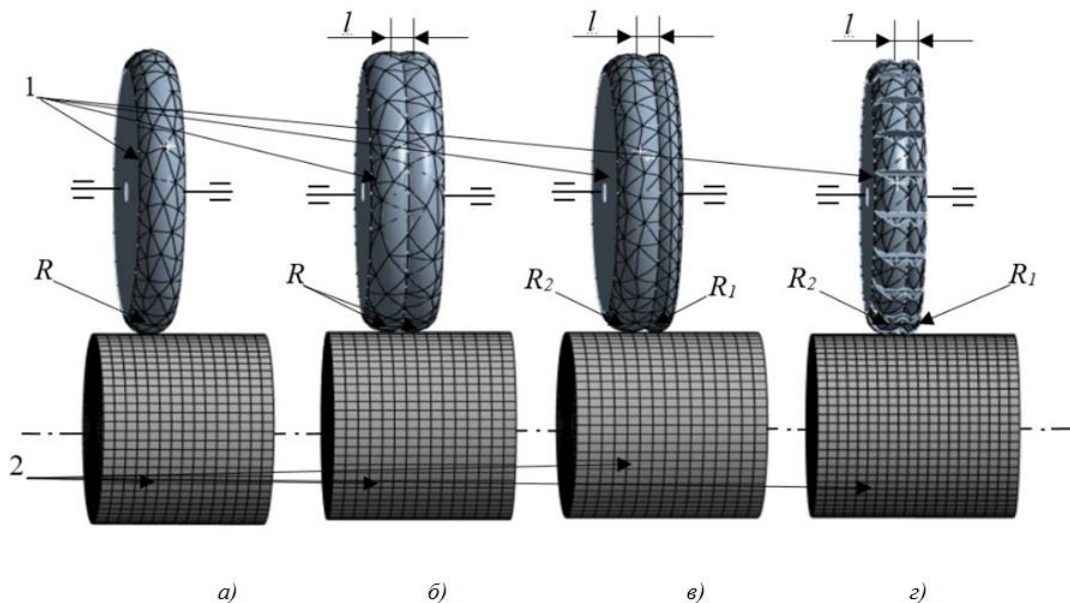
Конечно-элементные модели поверхностного пластического деформирования: 1 – торoidalные ролики; 2 – заготовки. Ролики: однорадиусный (а); двухрадиусный (б); двухрадиусный с разными радиусами скругления (в); торoidalный из чередующихся секторов с разными радиусами скругления (г)
